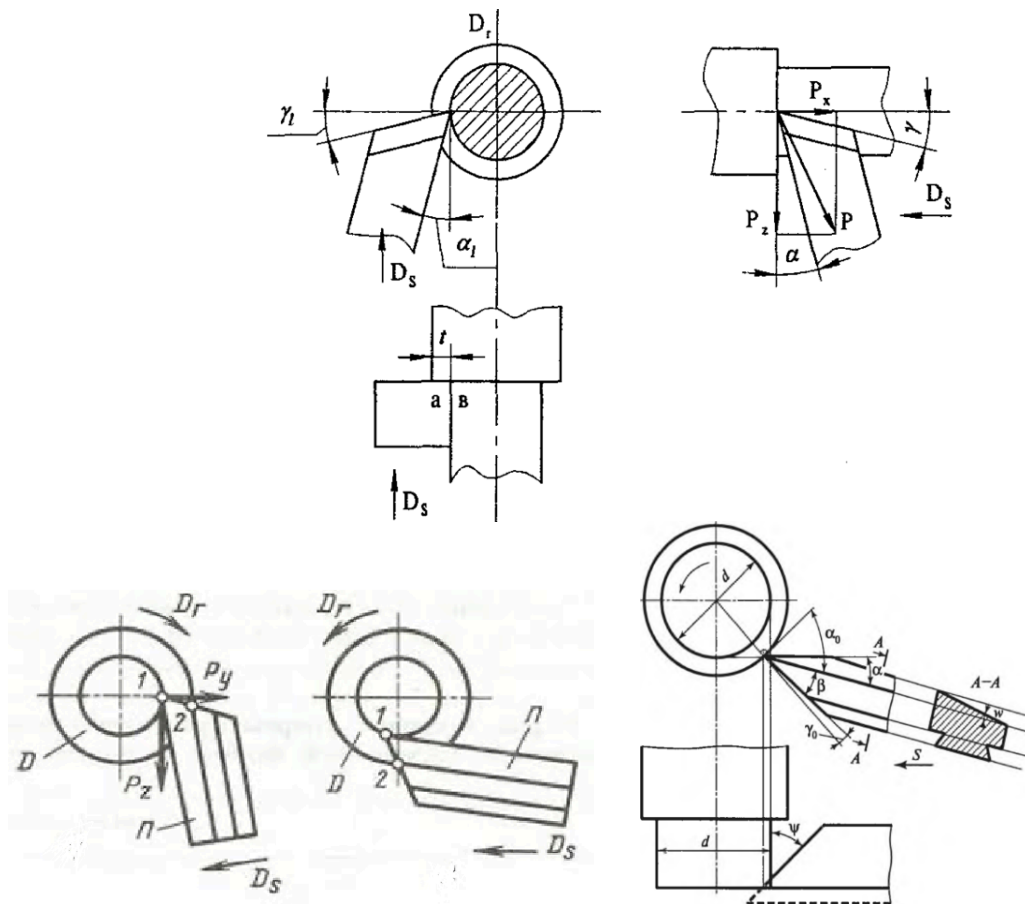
Установлення тангенціального різця щодо оброблюваної деталі
